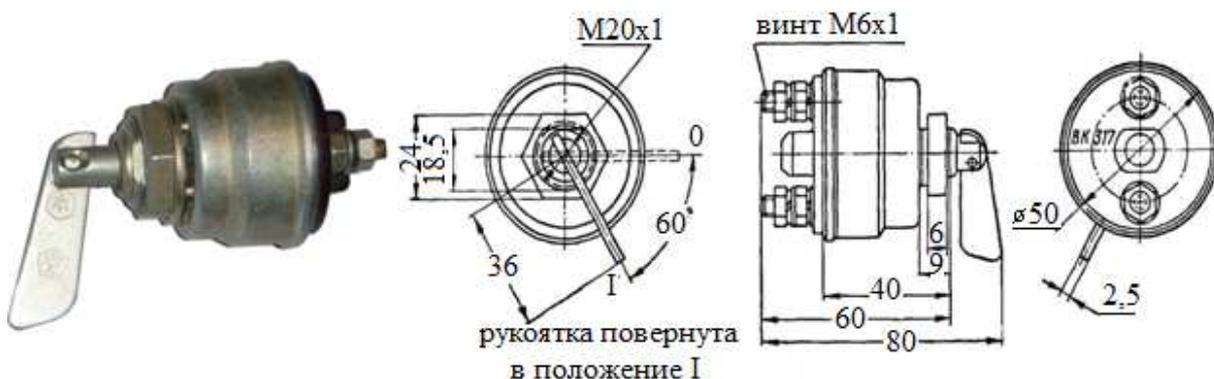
ВК-317, внешний вид и геометрические размеры
